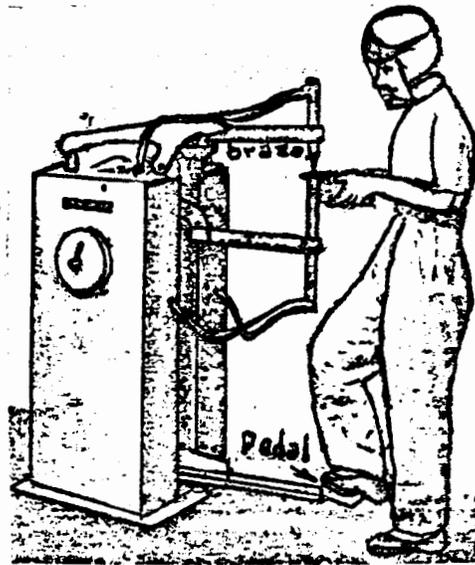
A. SOLDADORA DE BRAZO OSCILANTE.
